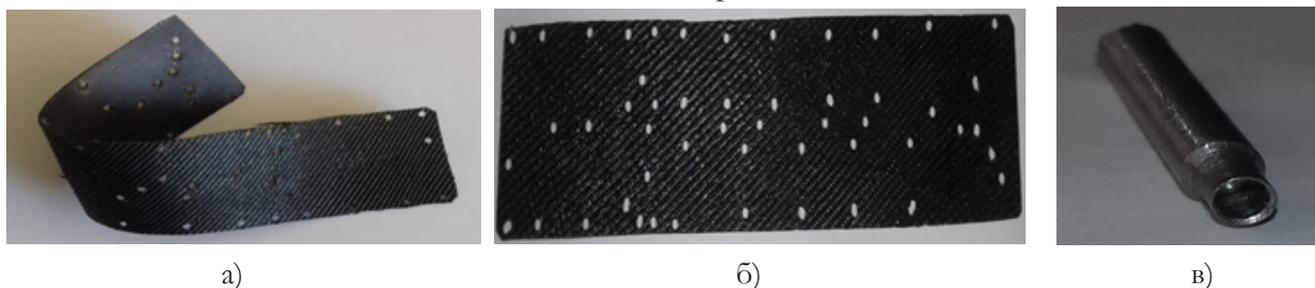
а) образец пропитанный эласилом, б) образец пропитанный эпоксидной смолой, в) приспособление для вырубки.
